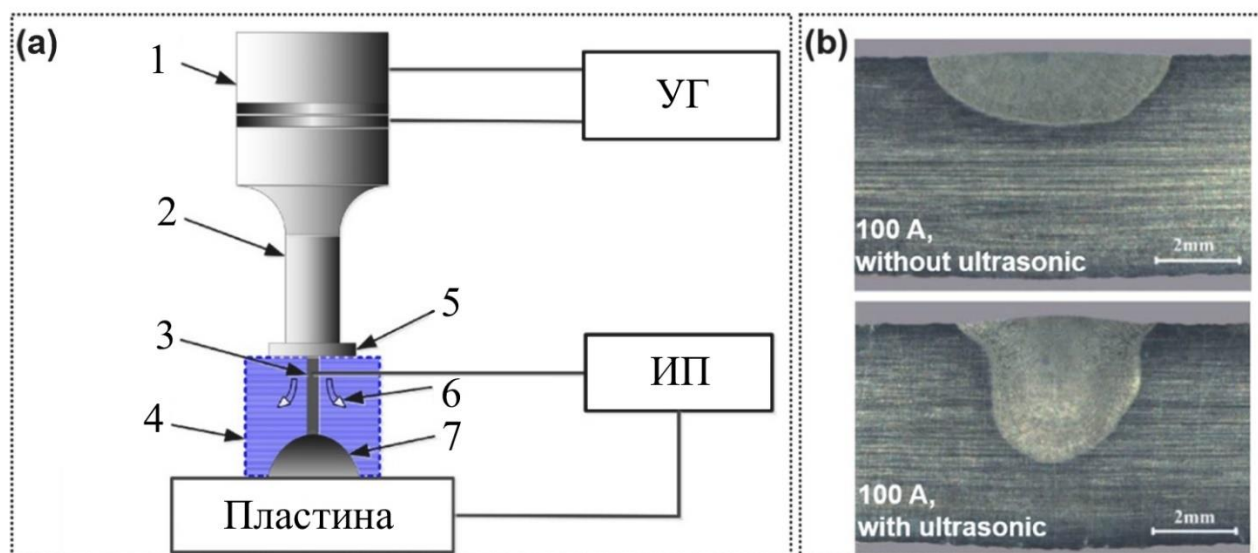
Схема U-GTAW (a) и макрошлифы проплавлений (b) [39]:
